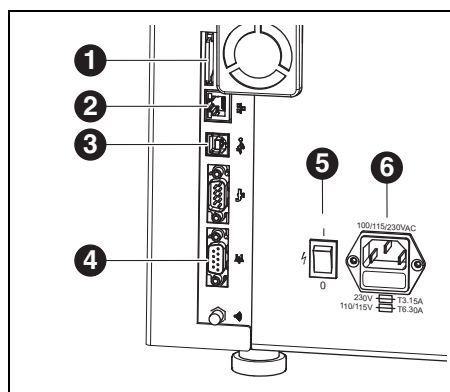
Interfaces sur la face arrière de la fraiseuse
